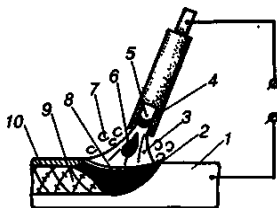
Схема процесса ручной дуговой сварки покрытыми электродами
